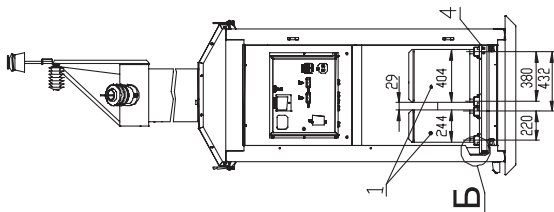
Общий вид сверху с двумя ВДР (вариант К.14)
